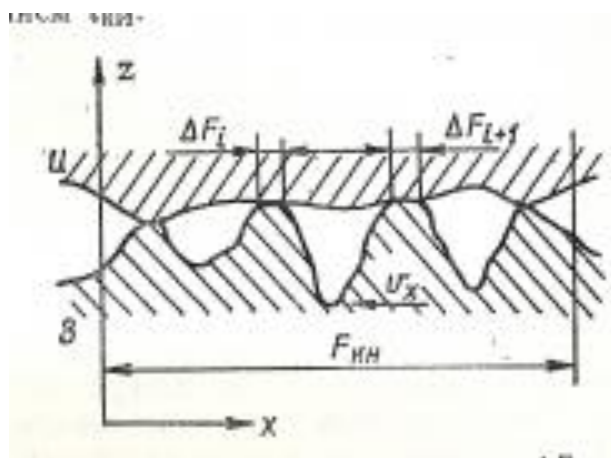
Схема взаимодействия элементов поверхностей деформируемой заготовкой (З) и инструментом (И)
